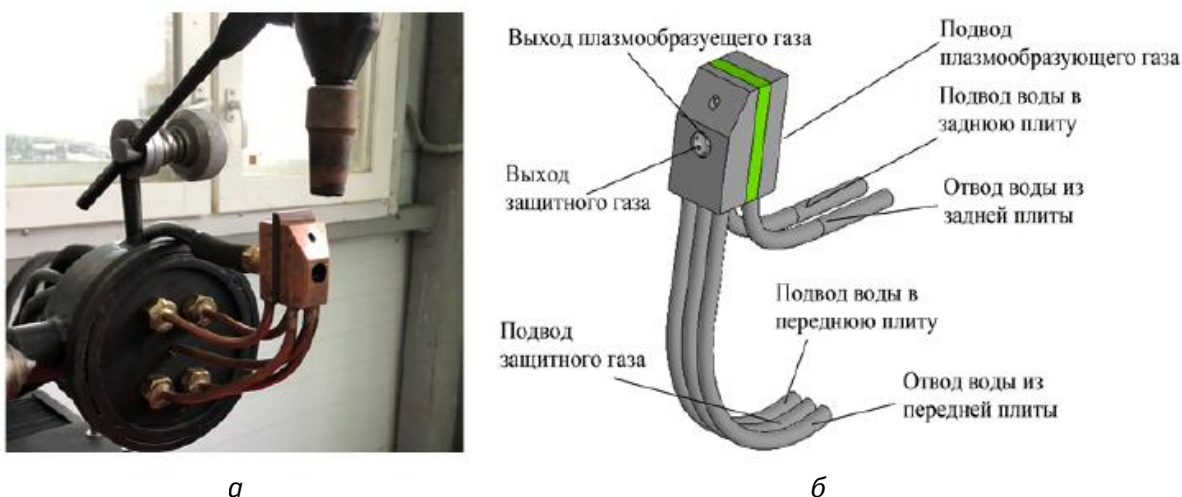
Базовый плазмотрон для плазменно-порошковой наплавки с внешней подачей порошка в дугу:
